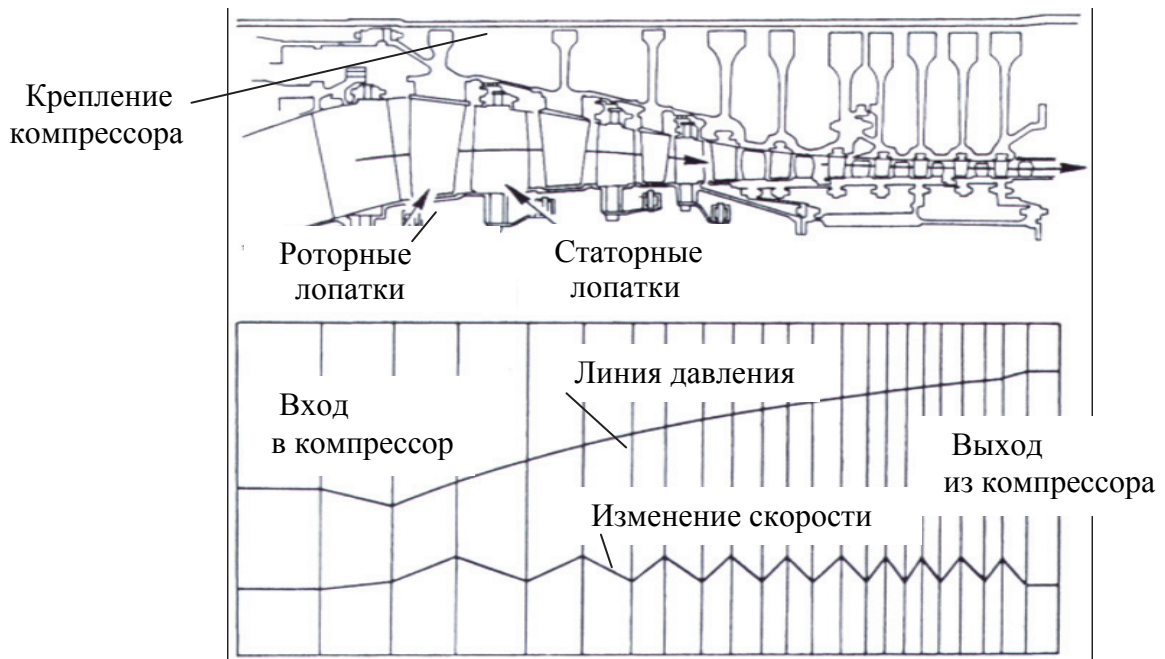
Проточный сужающийся канал осевого компрессора
